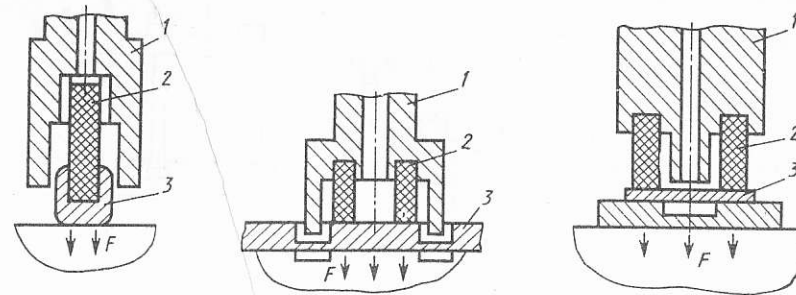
Схемы крепления заготовок при помощи упругих элементов
